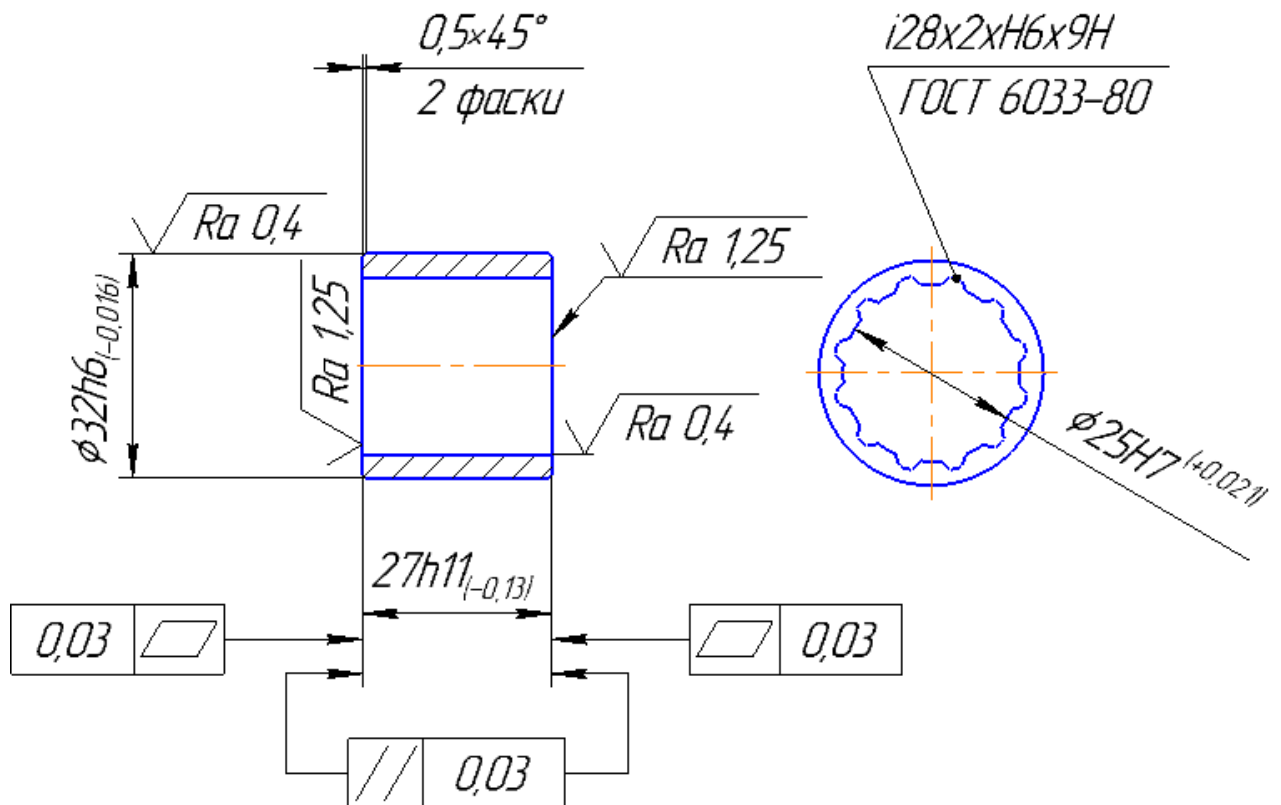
Втулка позиционная для установки подшипника шестерни пятой передачи
